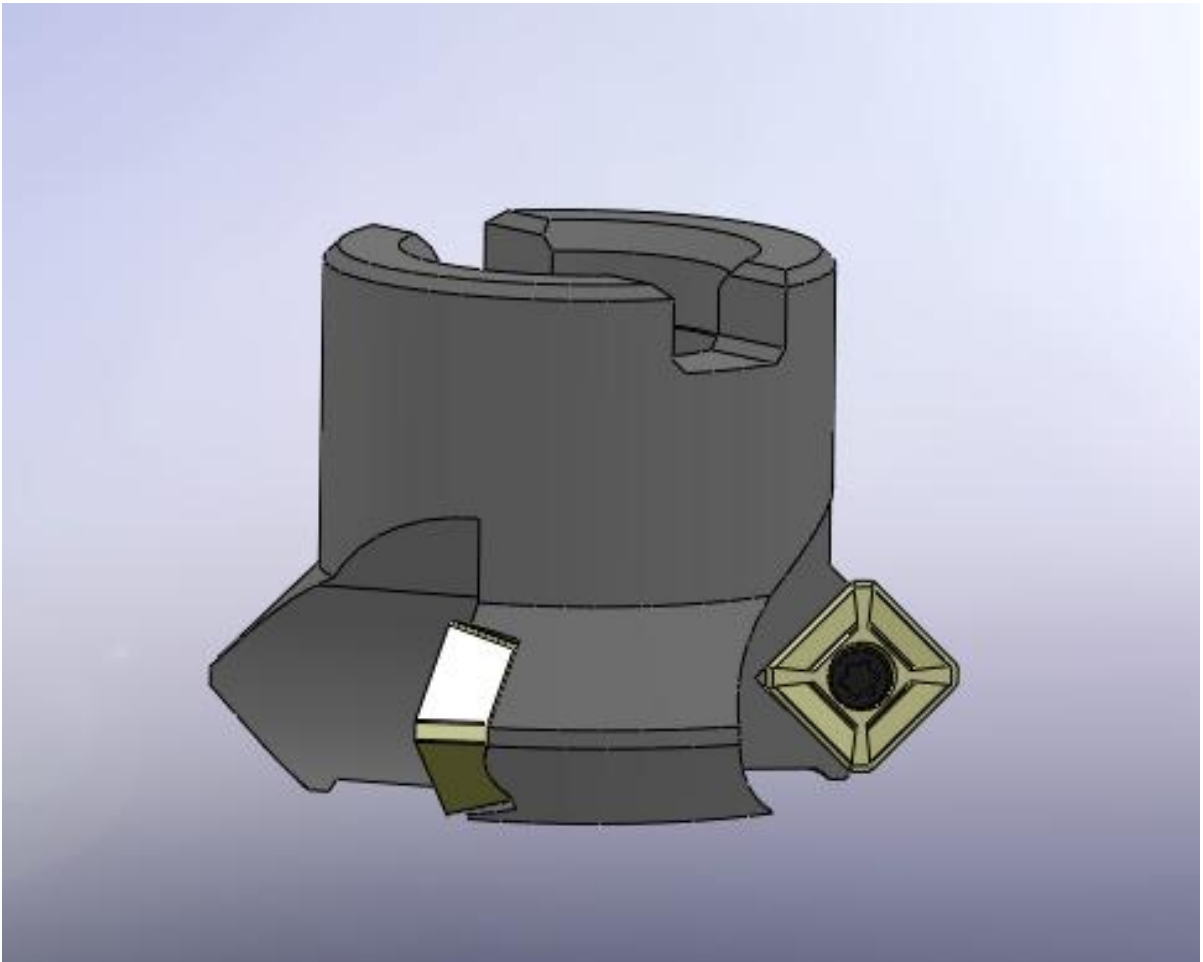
Загальний вид моделі нової запропонованої конструкції
